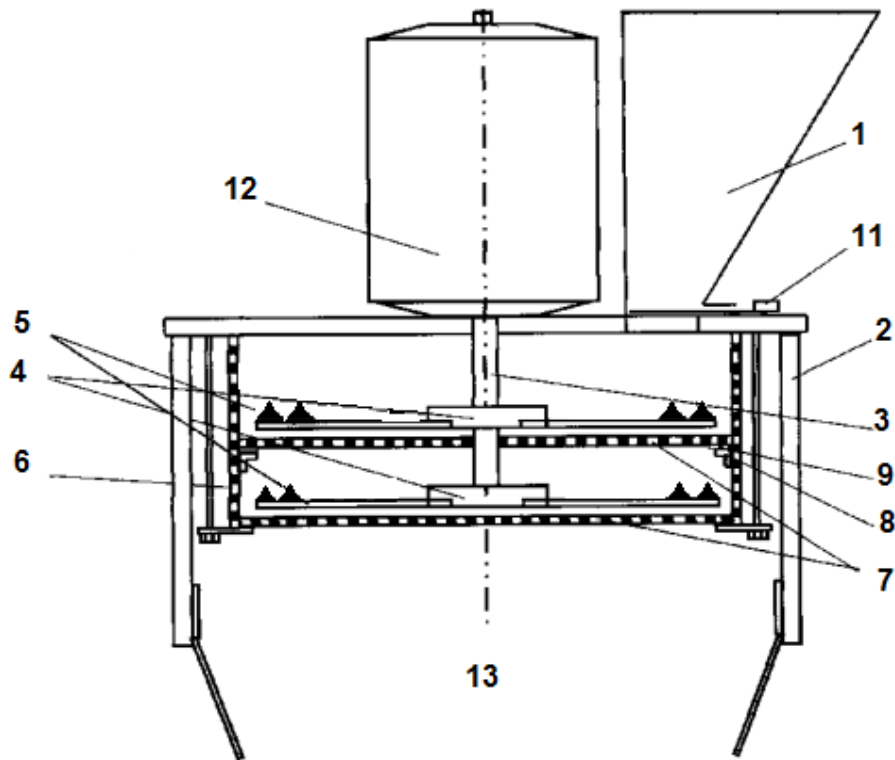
Подрібнювач ударно-відцентрової дії: 1 – завантажувальний бункер; 2 – циліндричний корпус; 3 – ротор; 4 – диски; 5 – плоскі молотки із зубами
